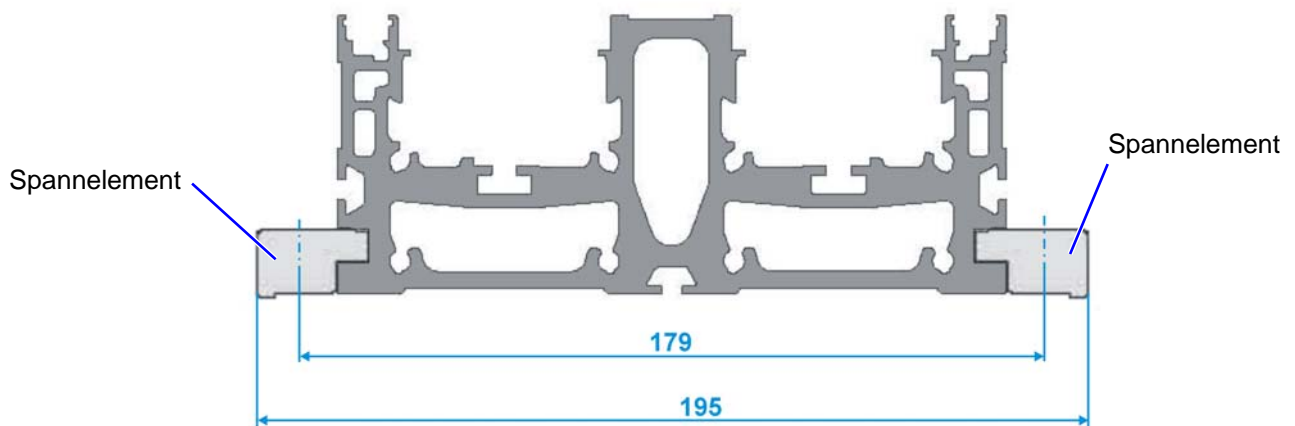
Querschnitt mit Spannelementen und Maßen (Modul 160/15)
